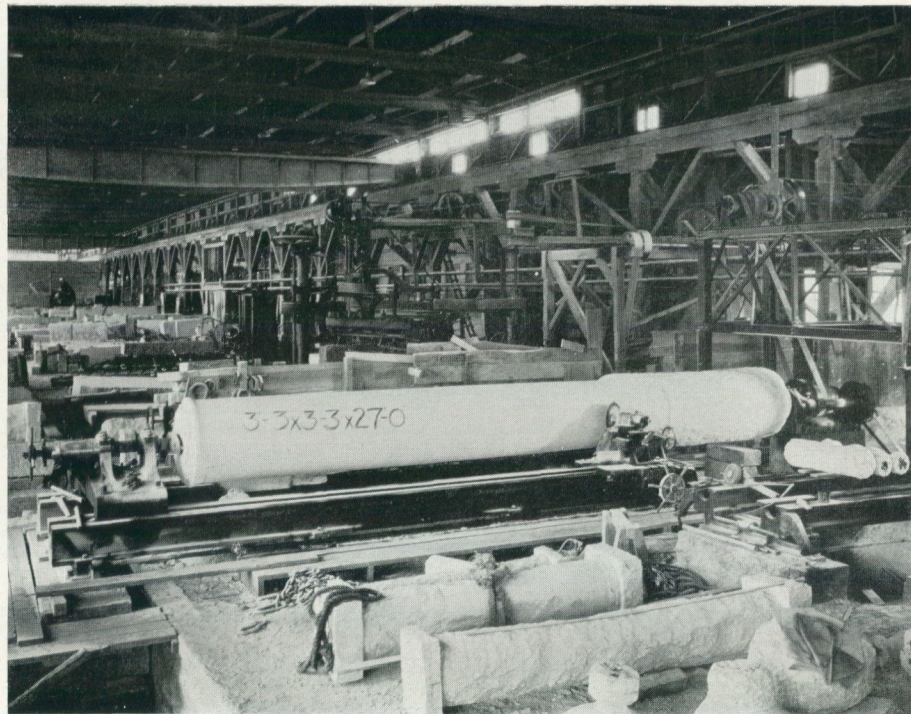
Granitsvarv i Mount Airy. Obs. Kolonnens dimensioner.
